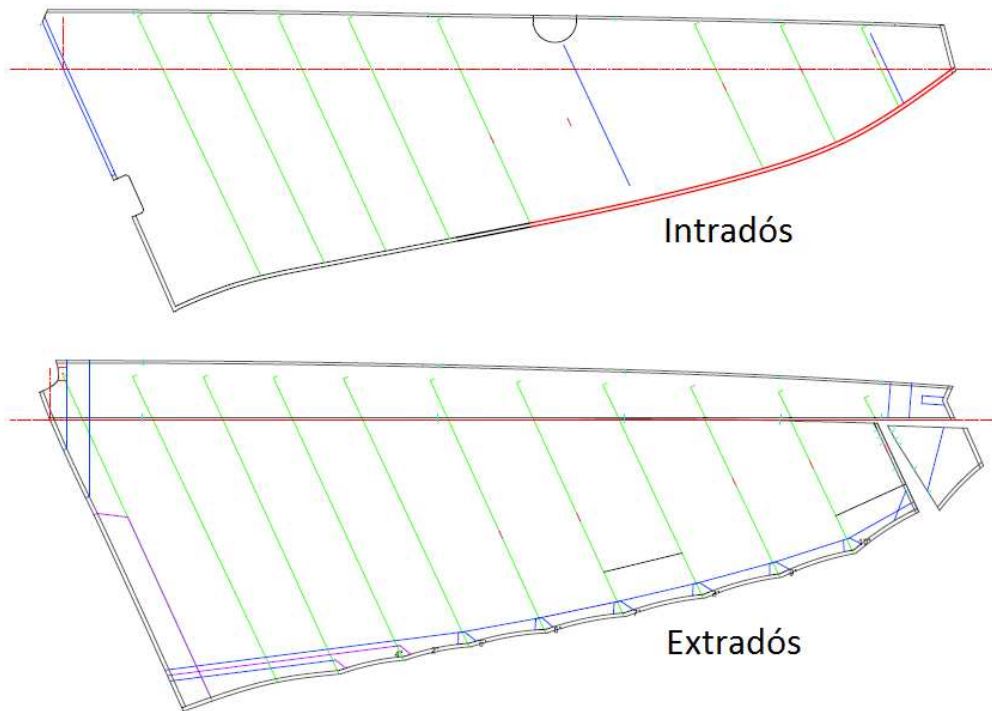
Planos de Paños de Tela de la EXTREME.
